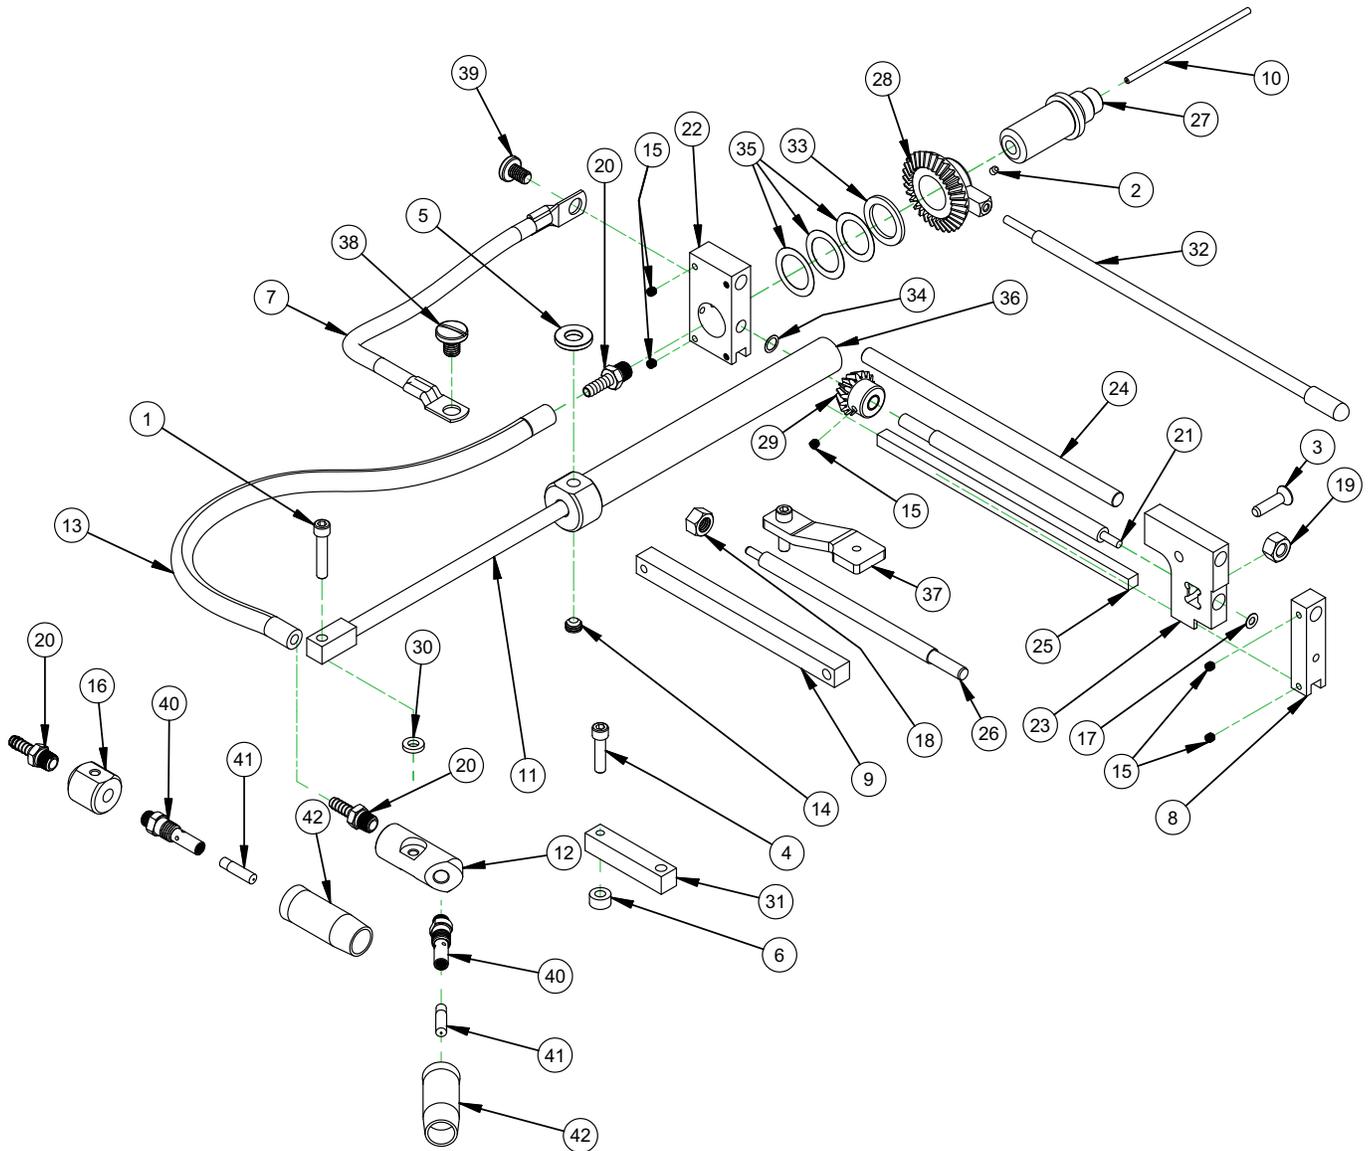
ENSEMBLE TORCHE DE SURFACE (203 MM) (RÉF. 28186)
